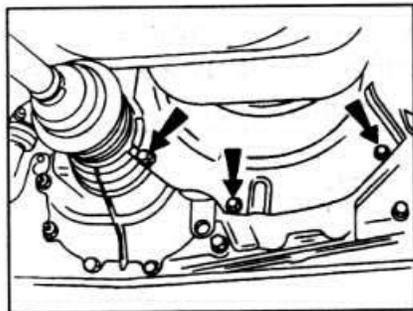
В.9. Расположение болтов крепления крышки маховика на коробке передач.
